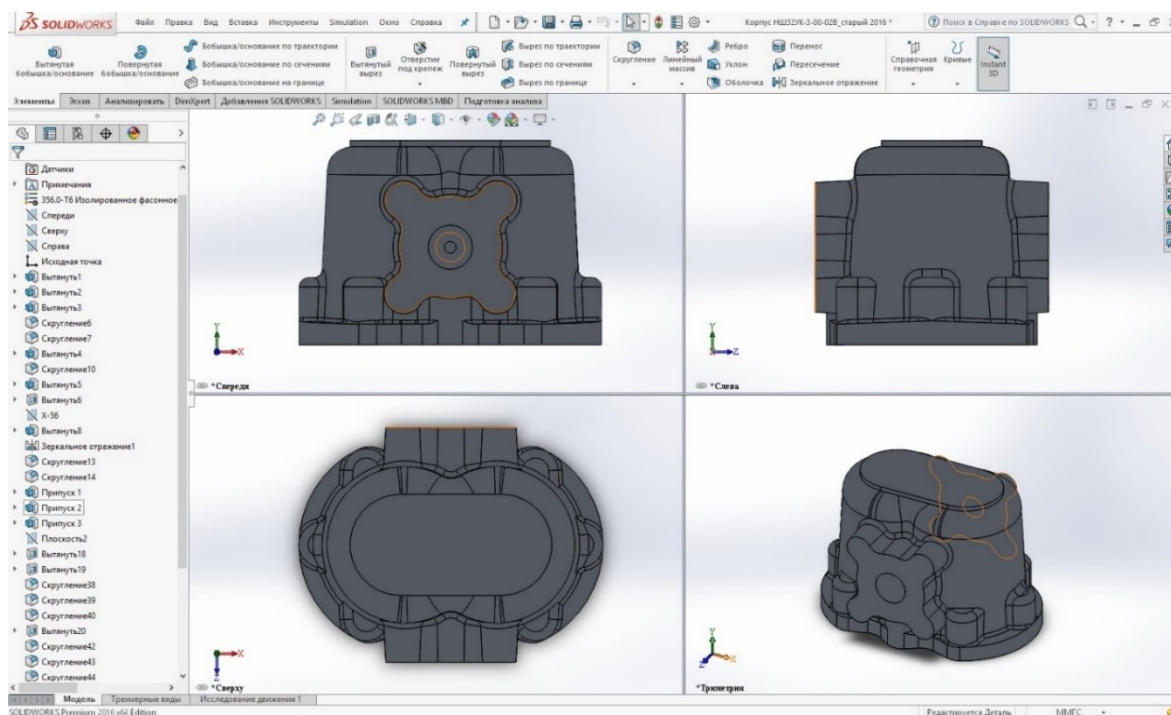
3D-модель виливка «Корпус НШЗ2УК»
